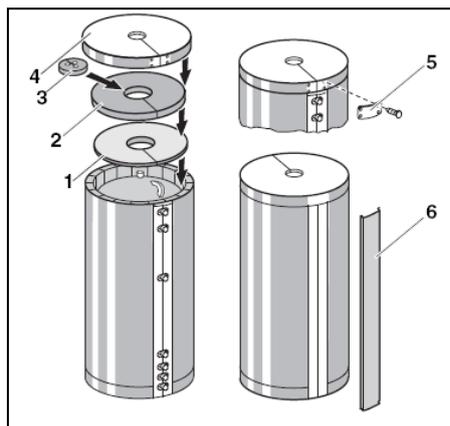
Монтаж теплоизоляции (принципиальная схема)
